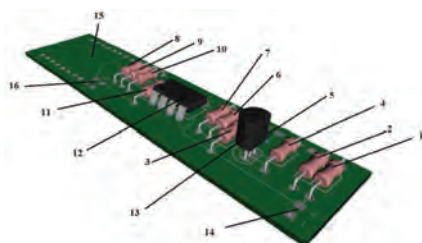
Внешний вид печатной платы с условными обозначениями
